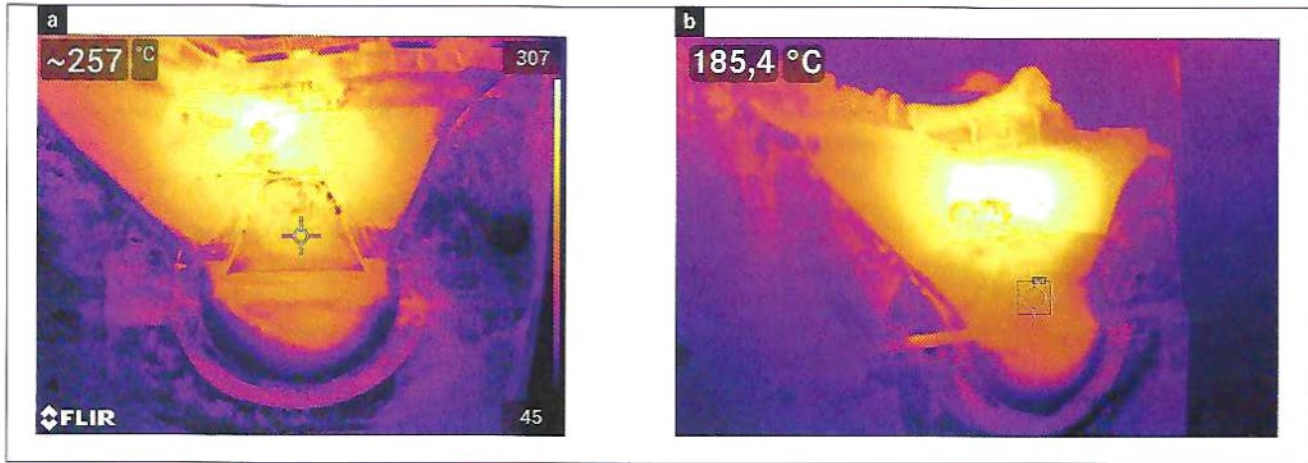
Der eindrucksvolle Nachweis für die deutlich schnellere Wärmeabfuhr: mit a) dem konventionellen Kühlkonzept heizt sich die Form um 72 °C mehr auf als mit b) DuraCool.
